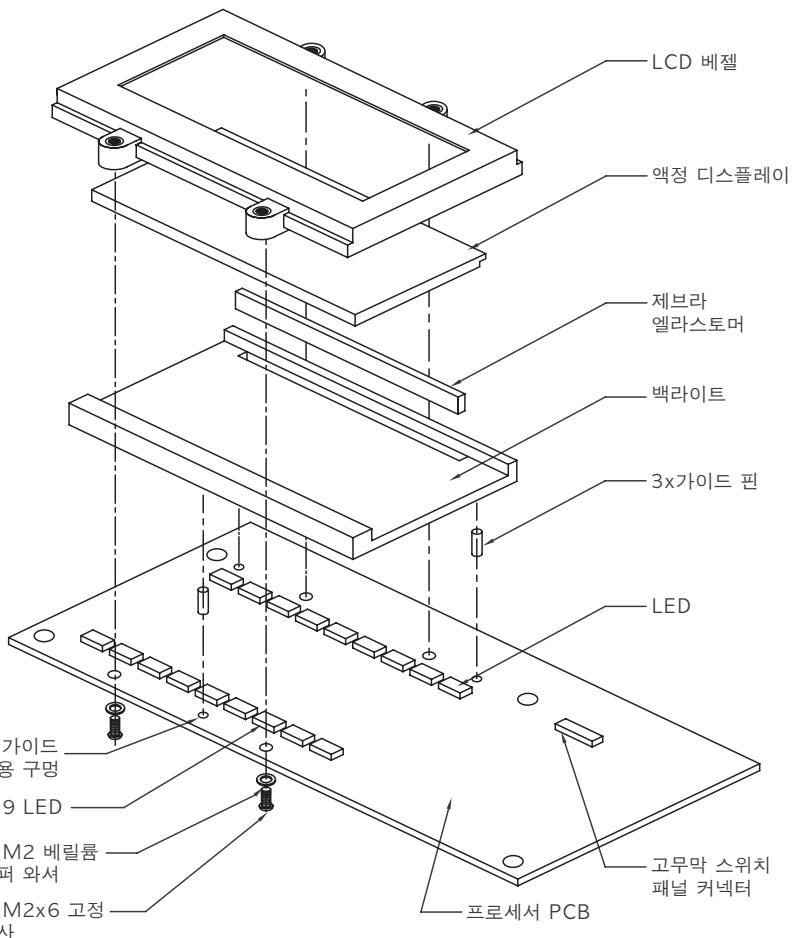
프로세서 PCB V3 어셈블리의 분해도
